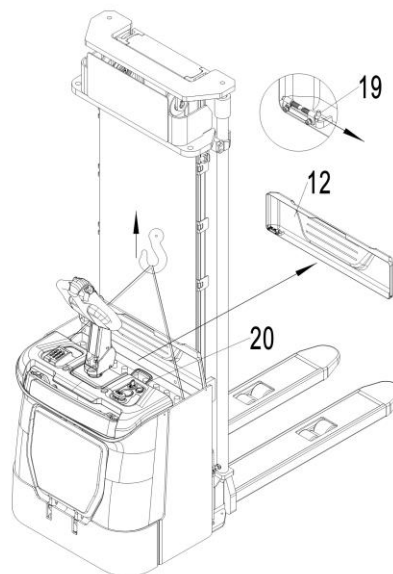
Sustitución de la batería sin colocar la batería de lado.
